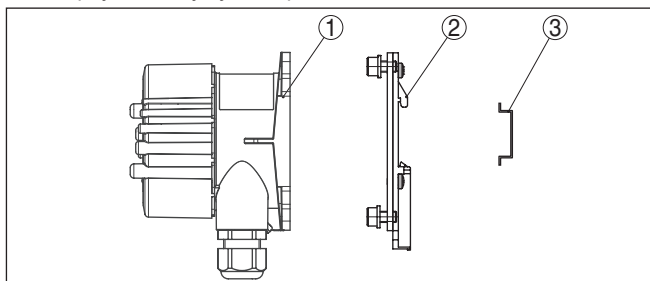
VEGADIS 81 с корпусом из алюминия или нержавеющей стали, для монтажа на несущей рейке
